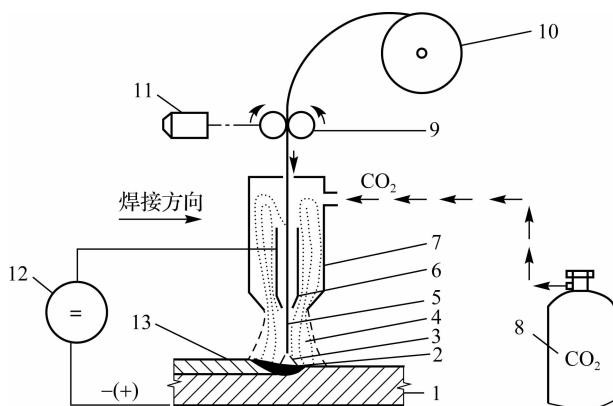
二氧化碳气体保护焊的焊接原理
